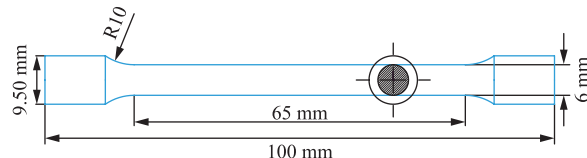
X80 管道环焊缝材料棒状拉伸试样尺寸图
